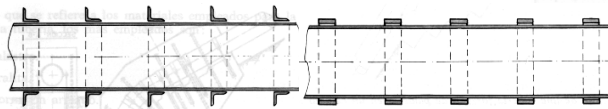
a-Tuberías zunchada, se refuerza las tuberías por anillos con hierro, b- Tuberías brindadas, se monta exteriormente en caliente anillos de refuerzos de sección rectangular y sin soldaduras que al enfriarse quedan aplicados fuertemente a presión sobre la tubería.
